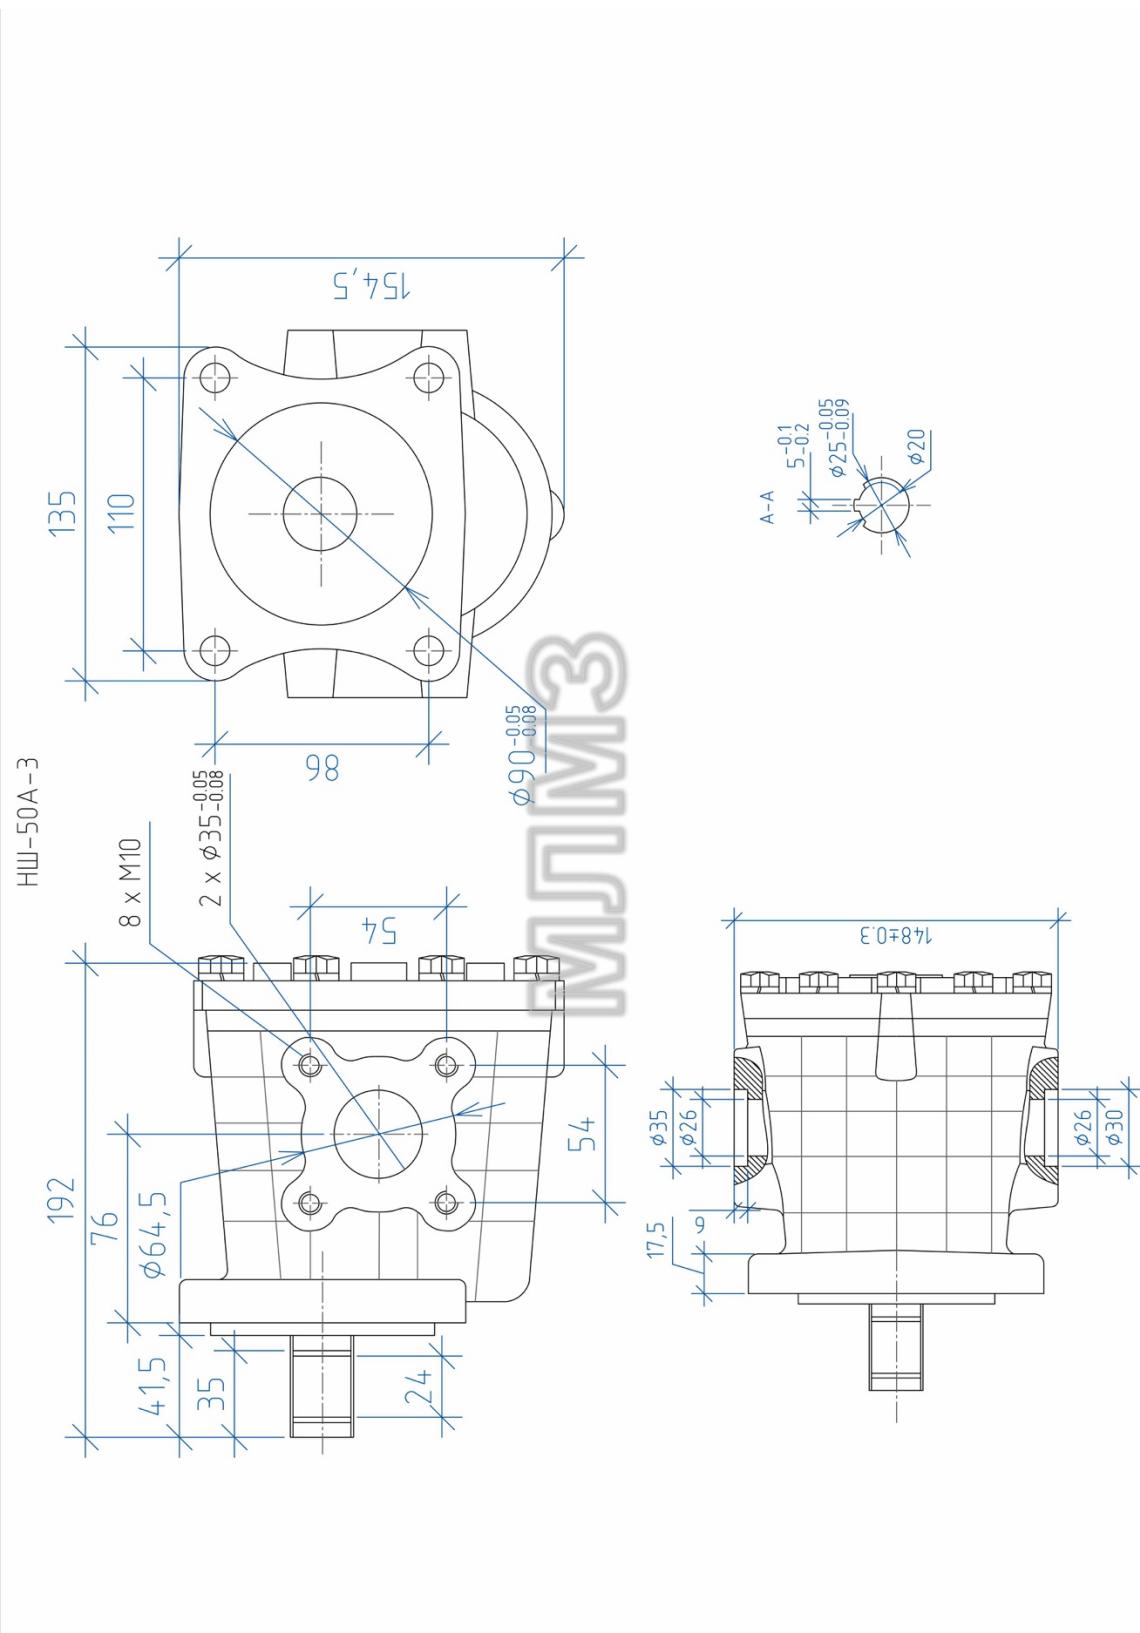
Насосы шестеренные НШ50А-3, НШ50А-3Л.Габаритные и присоединительные размеры.
